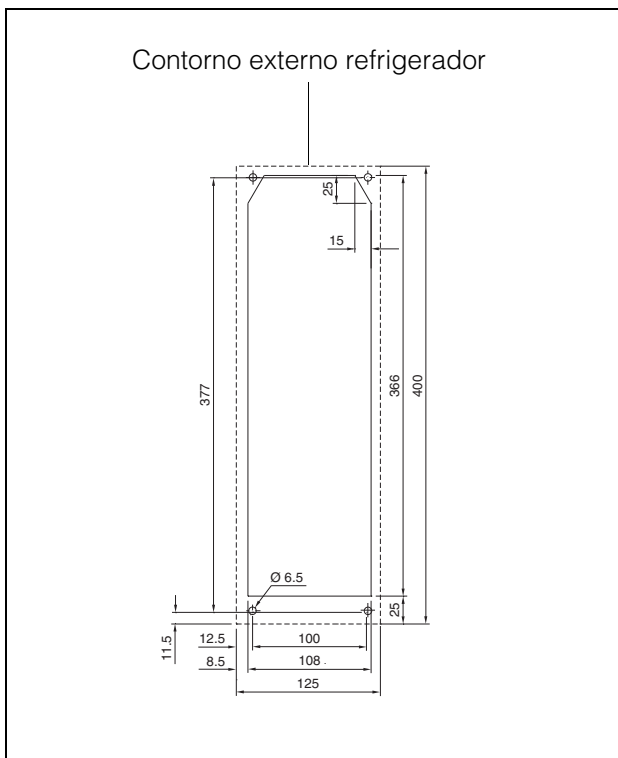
Escotadura de montaje y medidas de taladro con montaje exterior del aparato
